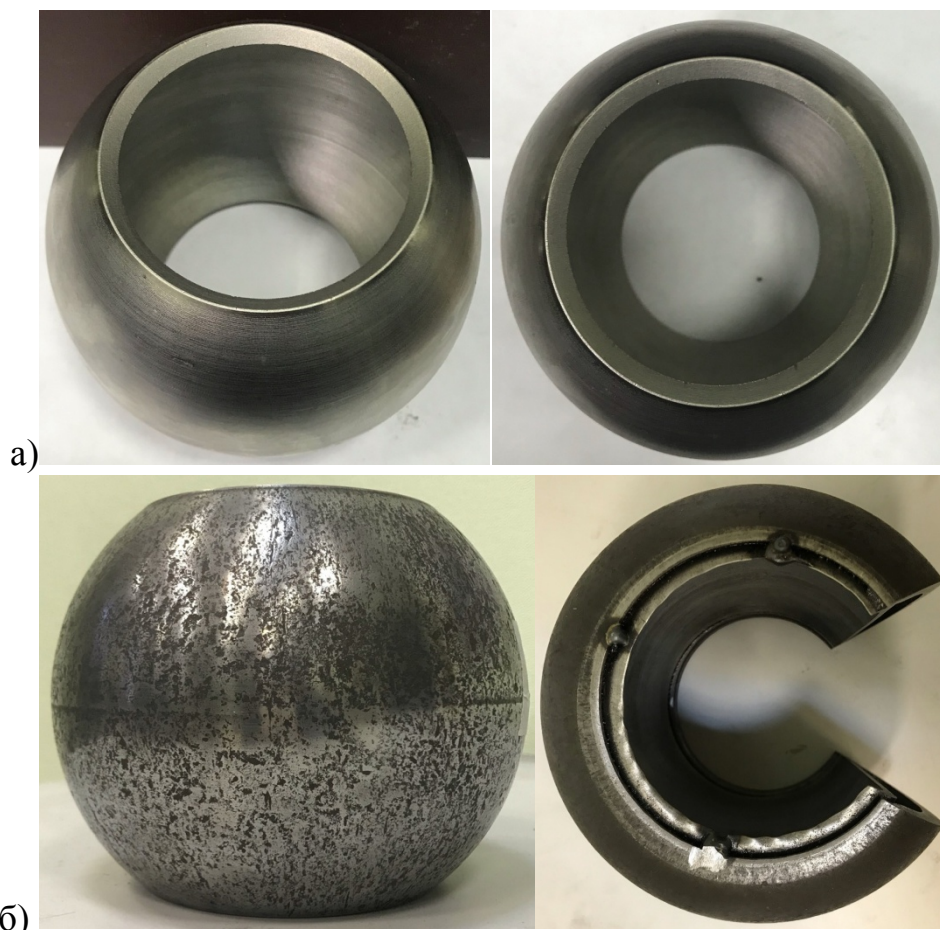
Внешний вид сферических пробок DN100 без патрубка(а) и с патрубком(б) после обжига
